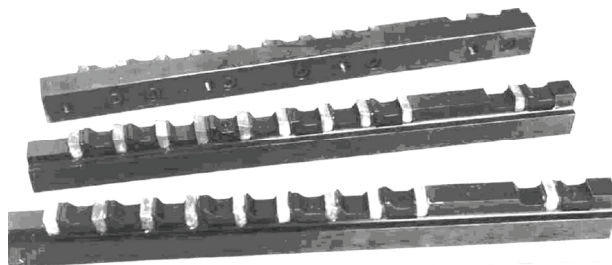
Общий вид сборной протяжки с вертикальным расположением режущих зубьев и клиновым зажимом
